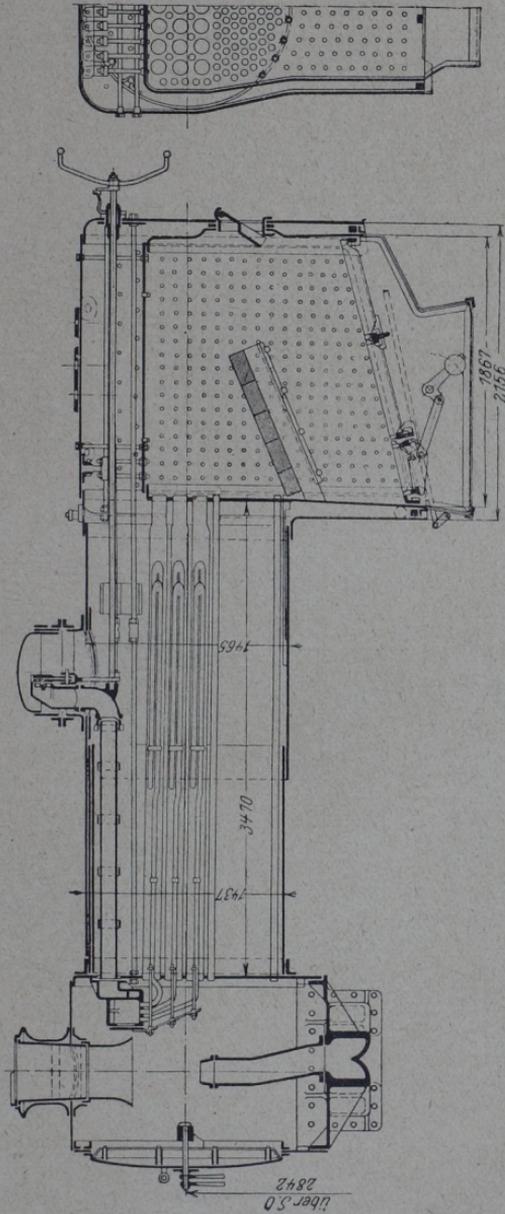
Englischer Kessel der 2B-Heißdampf-Zwilling-S-Lokomotive für die Hochland-Bahn.
